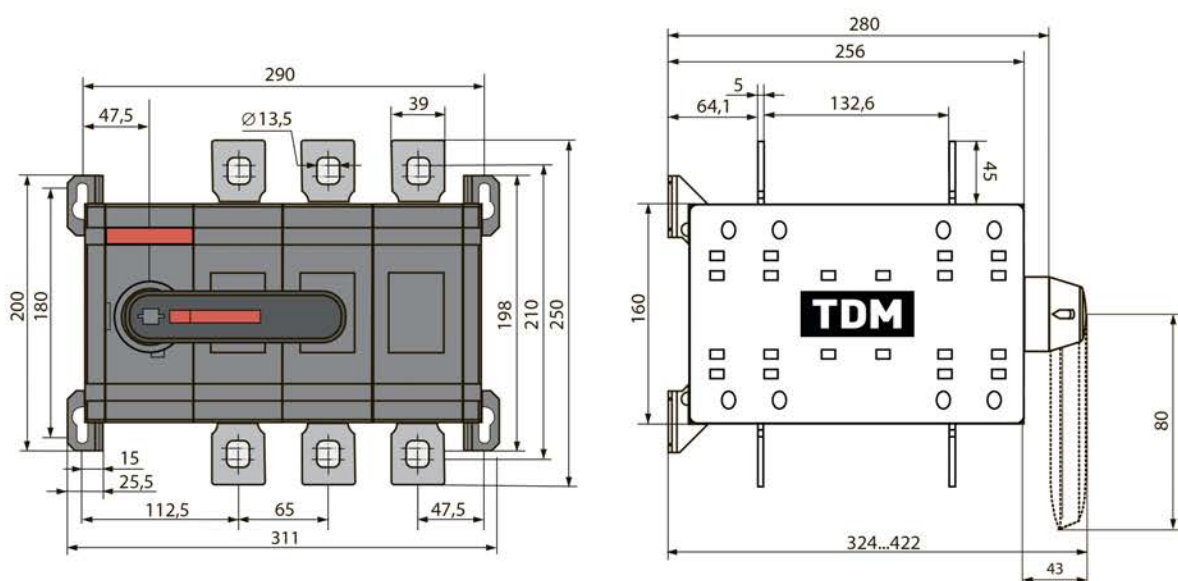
Габаритные и установочные размеры рубильника ВНК 39-1, мм
